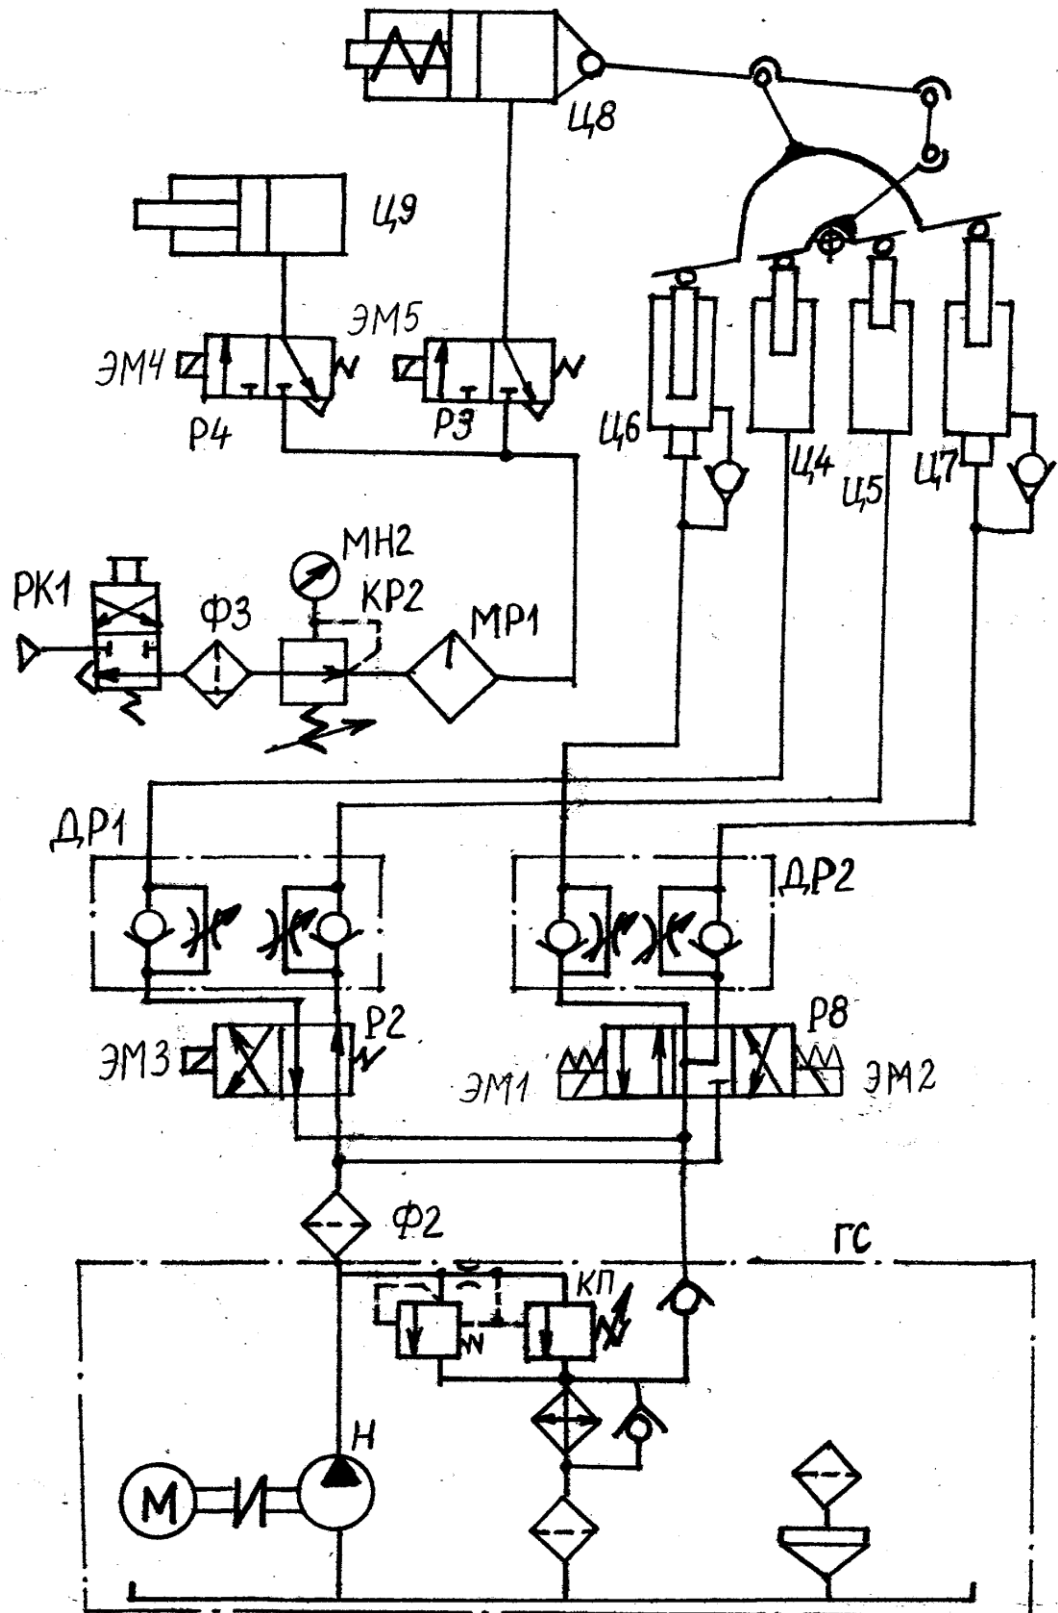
Гидропневматическая схема манипулятора для съема отливок
